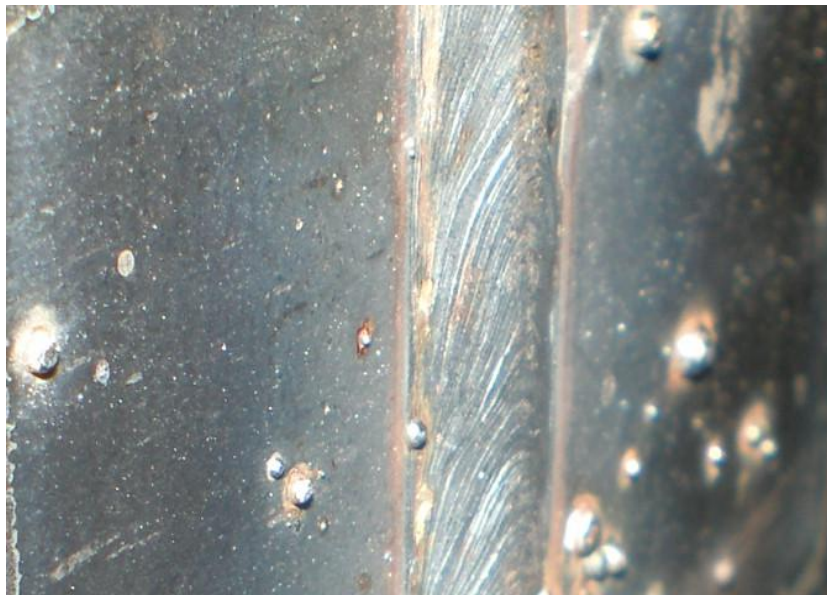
Probeta Acero AISI 1010 soldada bajo la condición de 160 Amp.
